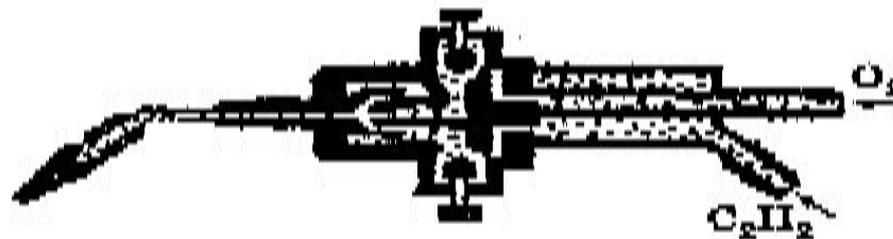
Инжекторная горелка для газовой сварки
